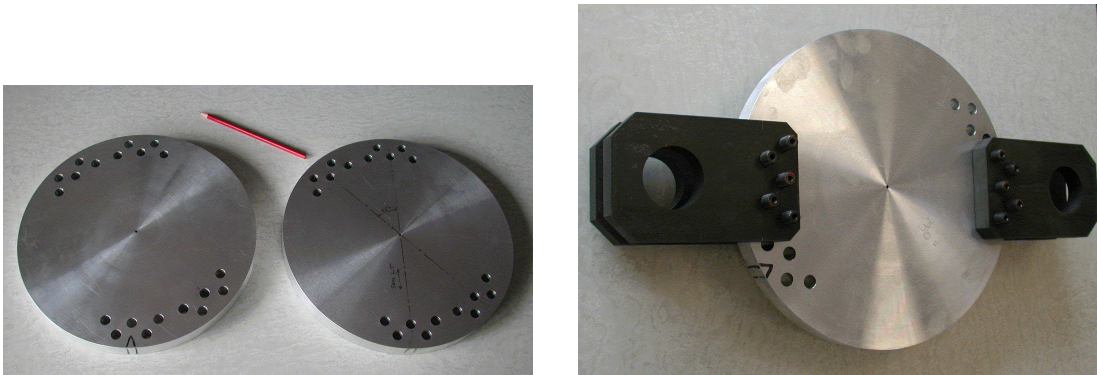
Géométrie de l'éprouvette cylindrique
